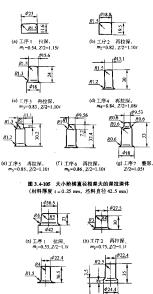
大小阶梯直径相差小的深拉零件(材料: 拉深钢板, 厚度 t = 0.5 mm, 坯料真径 66 mm)
